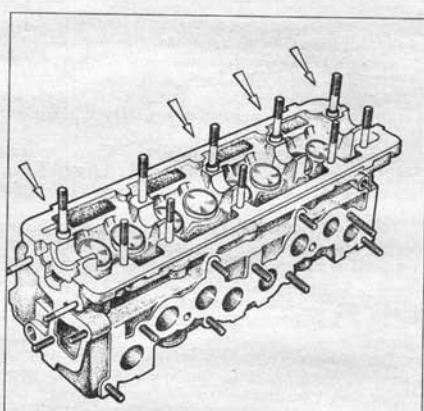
Установочные втулки корпусов подшипников распределительного вала
